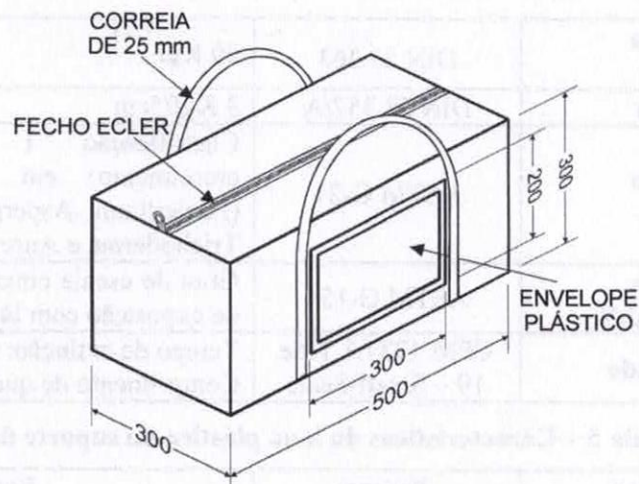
Bolsa para conexões estruturais (conexões e ferragens) (medidas em mm)
